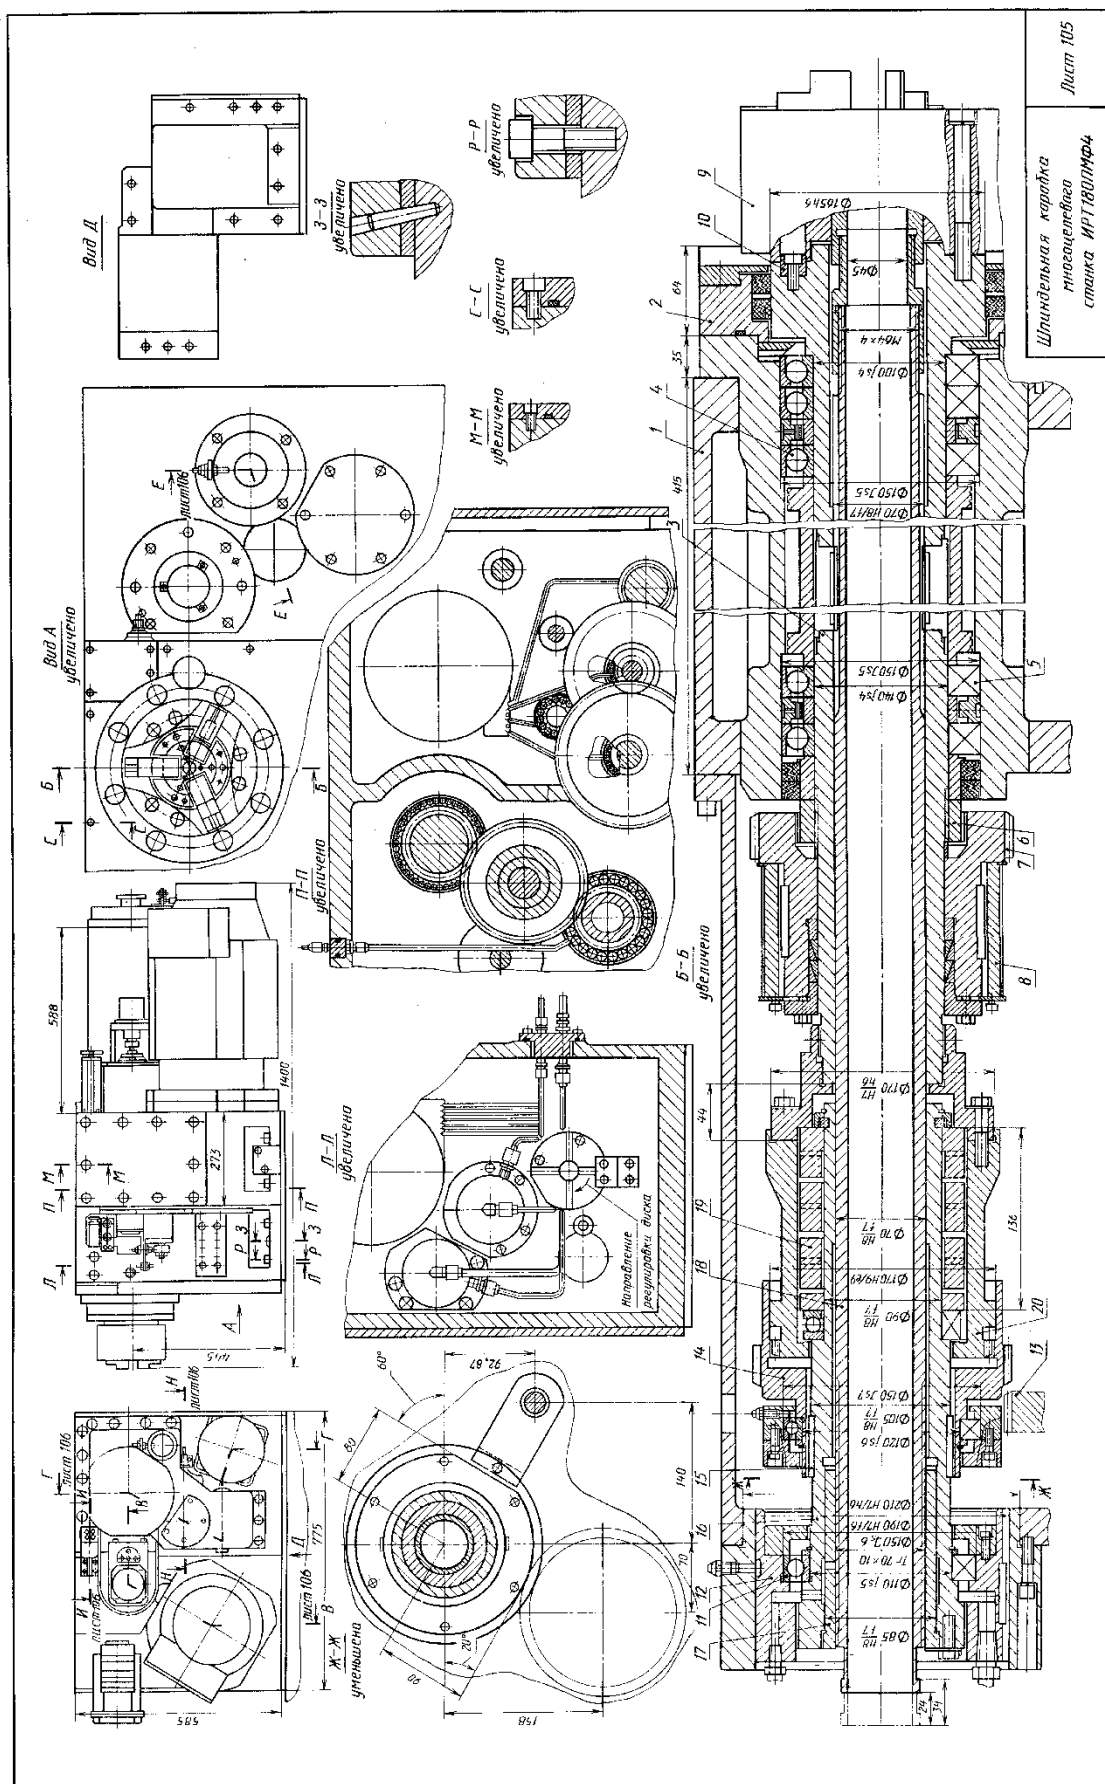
Шпиндельная коробка многоцелевого верстага ИРТ 180ПМФ4
